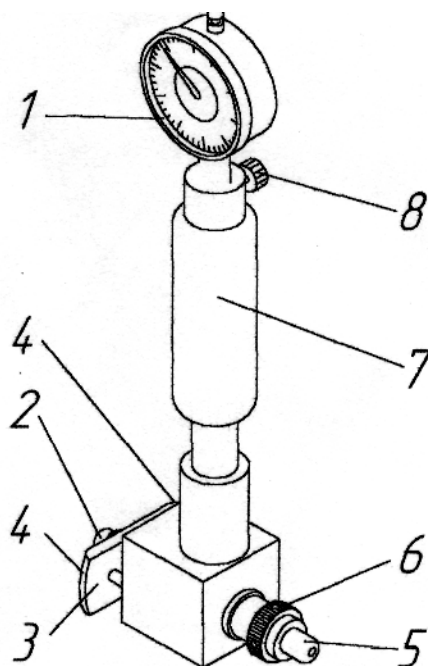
Нутромер со стрелочной отсчетной головкой и угловой передачей: 1 - отсчетное устройство, 2 - подвижный стержень, 3 - центрирующая планка (мостик), 4 - скругленные поверхности (опоры), 5 - неподвижный стержень, 6 - контргайка, 7 - ручка, 8 -винт
